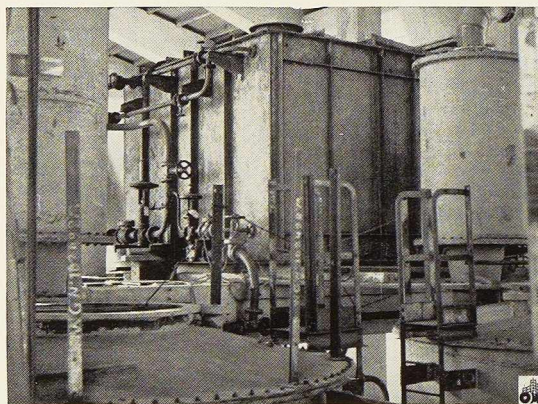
Vue d'un réservoir soudé, situé à une hauteur de 20 mètres.
